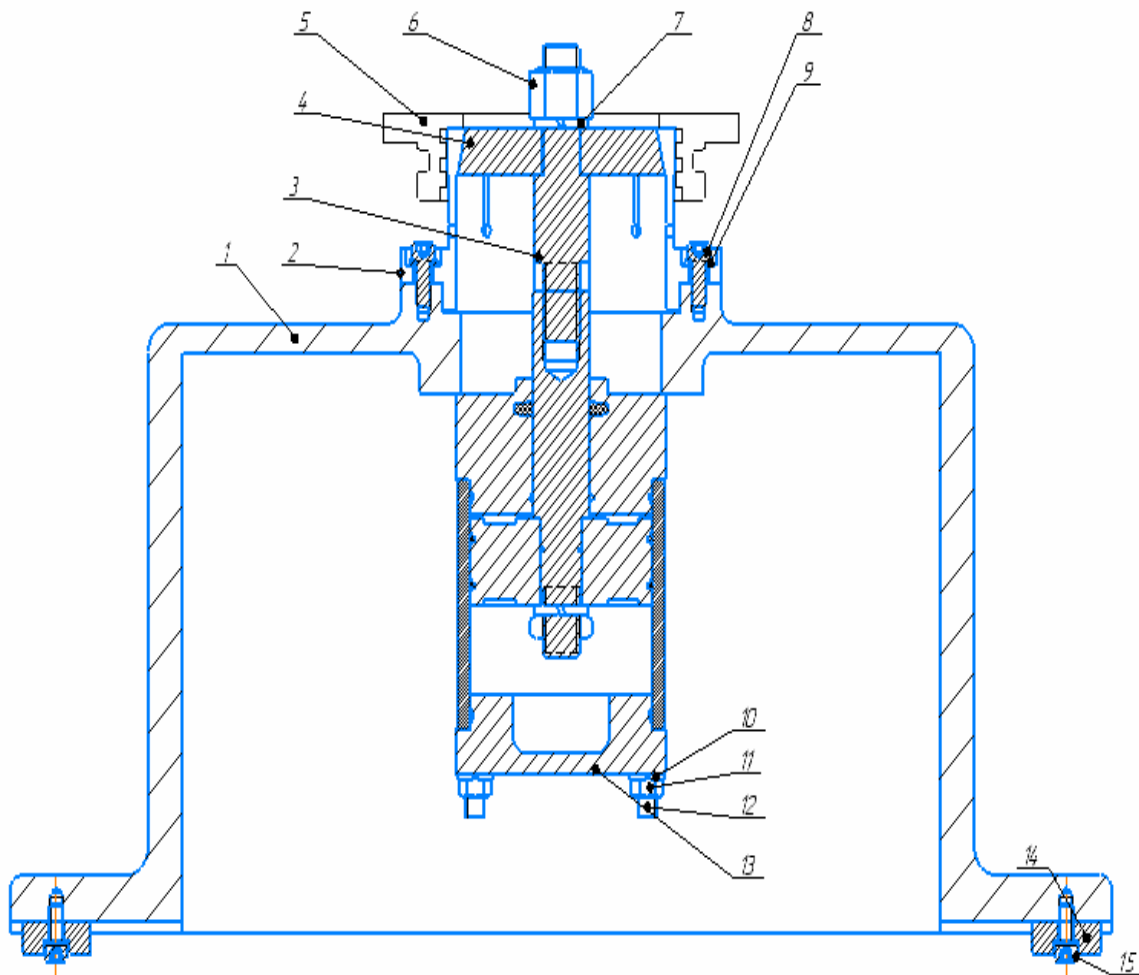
Приспособление для вертикально-фрезерной с ЧПУ операции
